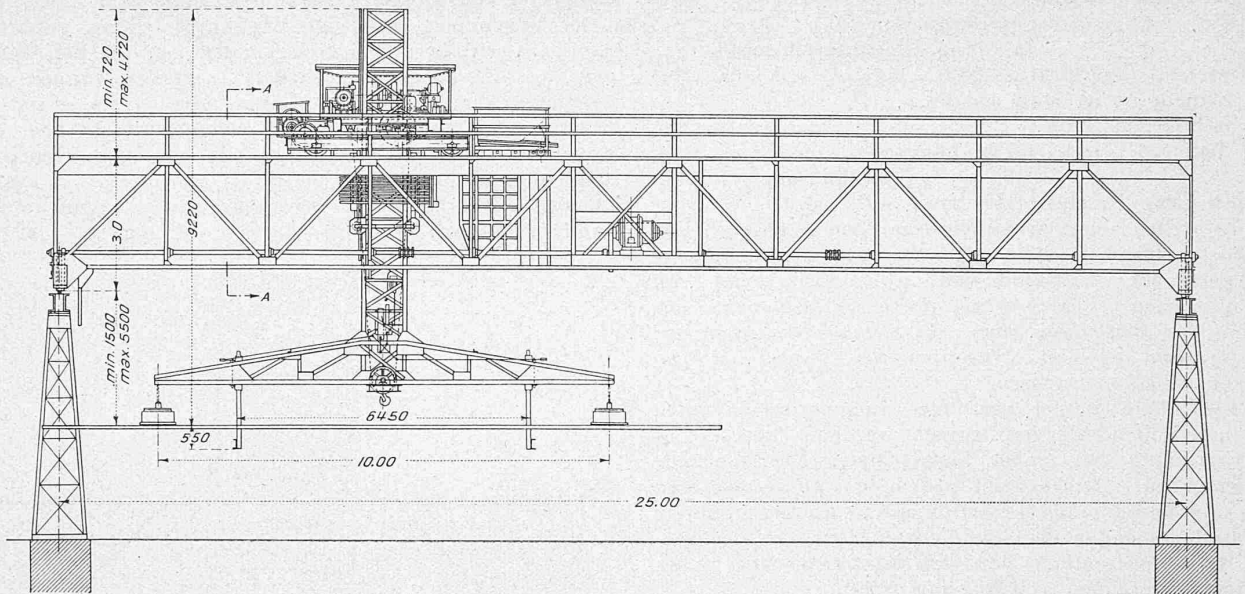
Laufkran mit Lasthebemagneten zum Transport von 20 m langen Walzeisen. — Gebaut von der Maschinenfabrik Oerlikon. — Masstab 1:150.
